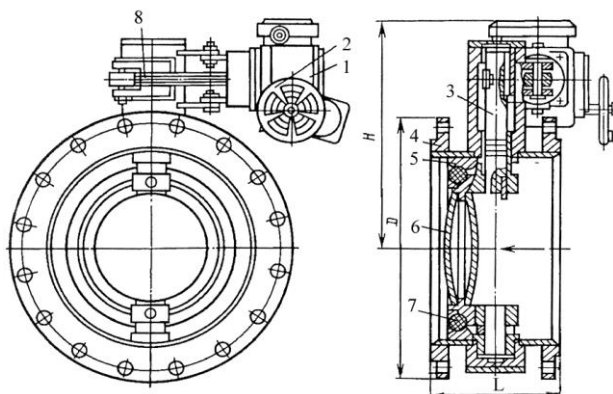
Дискový поворотный затвор с электроприводом: 1 – привод; 2 – ручной дублер; 3 – приводной вал; 4 – корпус; 5 – седло; 6 – диск; 7 – уплотнительное кольцо; 8 – шпindelь
